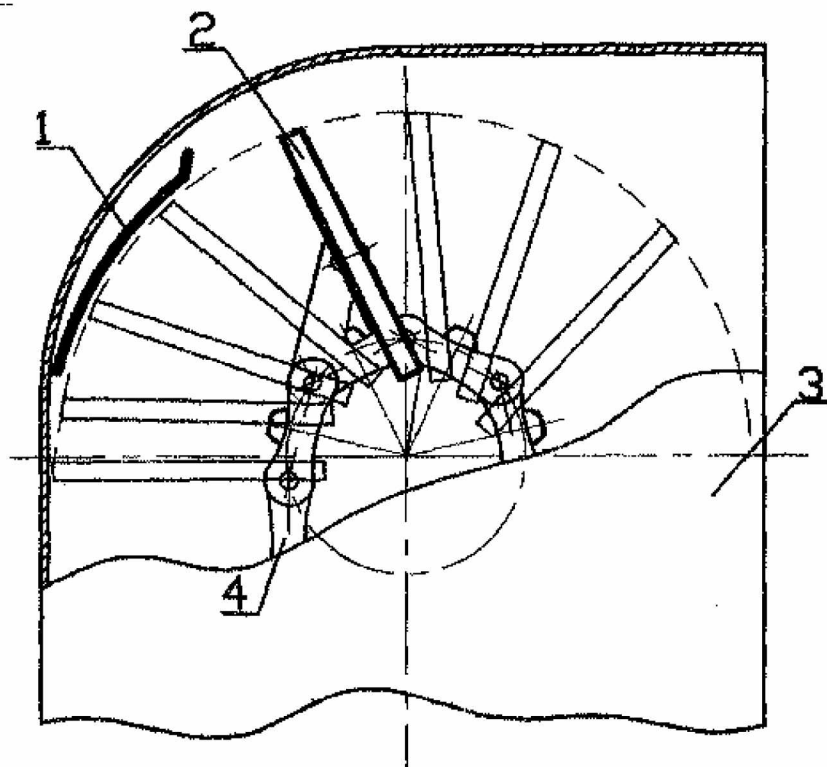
Схема дообладнання конструкції верхньої частини зернового елеватора додатковою напрямною криволінійною поверхнею: 1 – додаткова криволінійна поверхня; 2 – скребок; 3 – верхня частина елеватора; 4 – ланцюг зі скребками.
